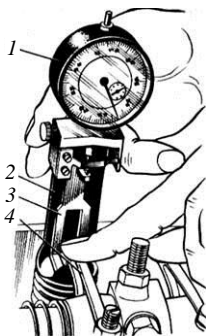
Измерение зазора приспособлением КИ-9918:
